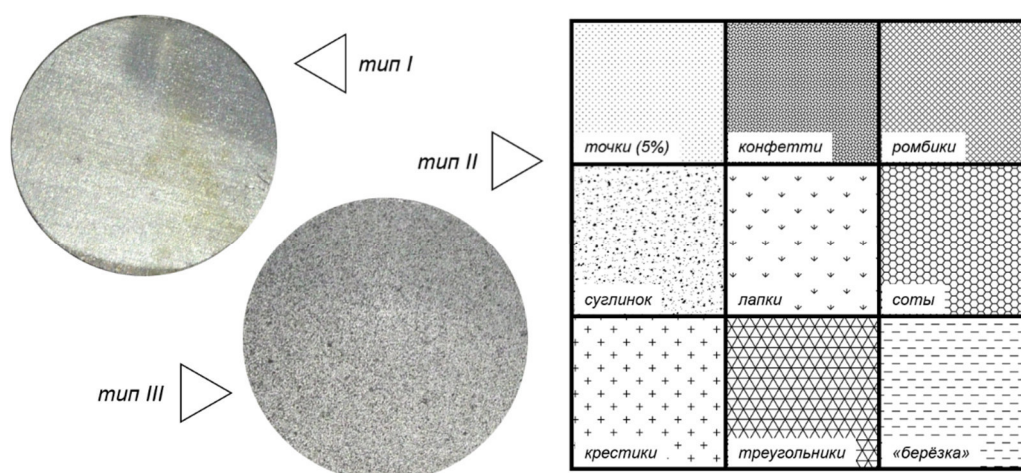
Изучаемые паттерны поверхности листовой заготовки
